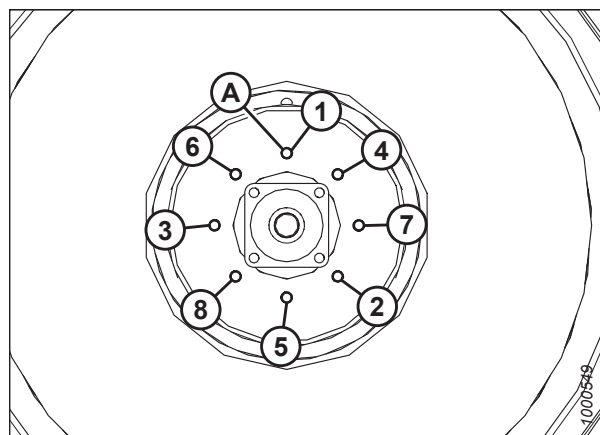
Вилочные самоустанавливающиеся колеса с подвеской
